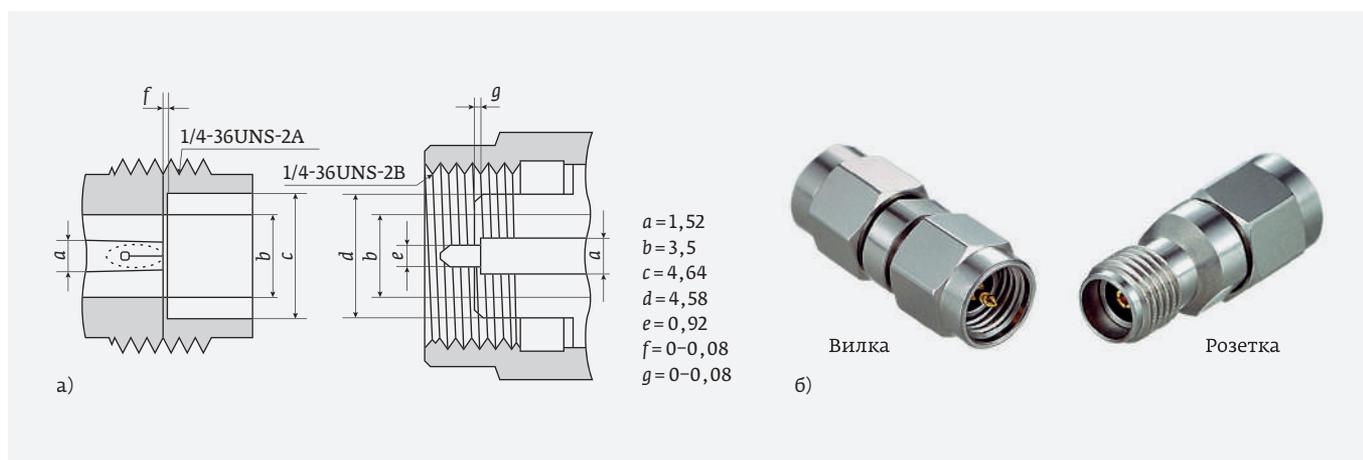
Интерфейс (а) и внешний вид соединителя 3.5 mm (б)
